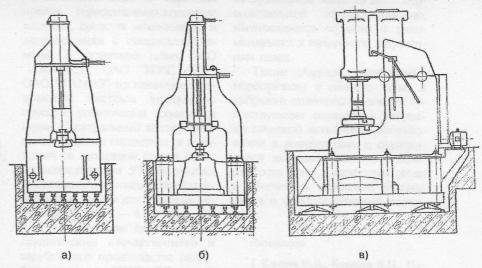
Конструктивные схемы виброизолирующих установок штамповочного (a), ковочного (b) и пневматического ковочного (b) молотов
